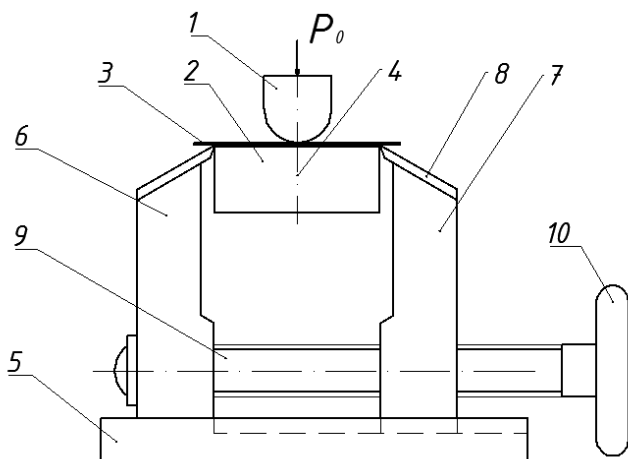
Затискний пристрій з взірцем: 1 – пуансон (призма овальна); 2 – взірець; 3 – шпон; 4 – лінія установки призми; 5 – основа пристрою; 6 – стріла стаціонарна; 7 – стріла рухома; 8 – ножі опорні; 9 – гвинт; 10 – маховик
